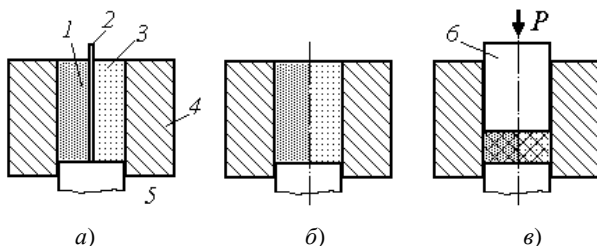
Схема прессования двухслойной прессовки с вертикальным расположением слоёв:
